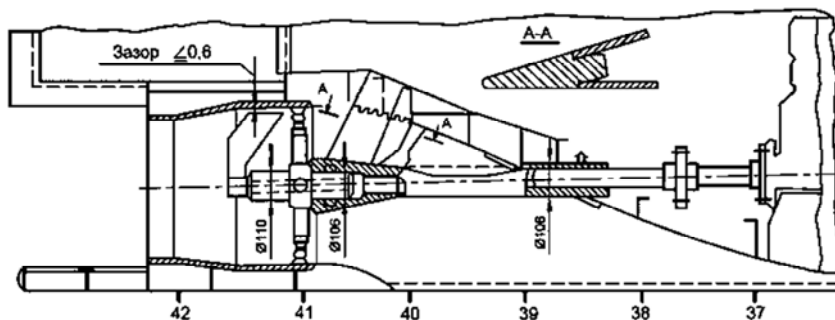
Установка приспособления для центрирования дейдвудной трубы
